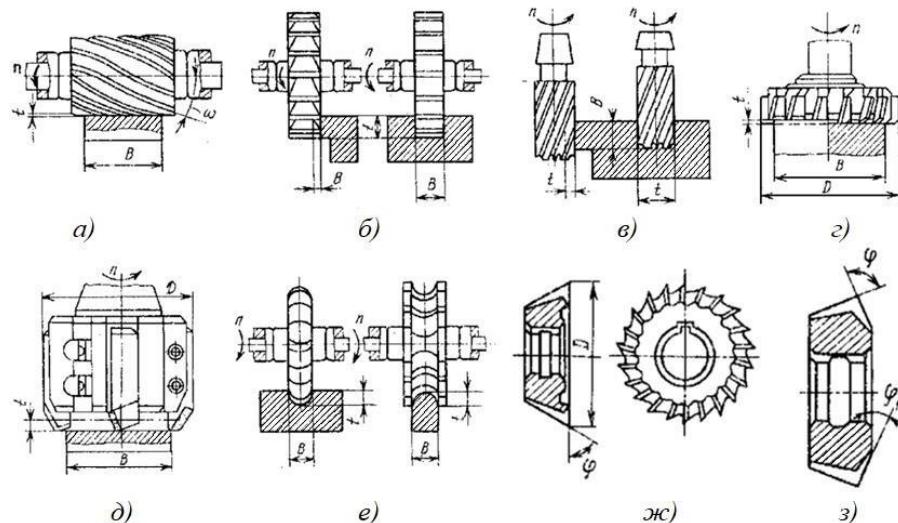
Типи фрез та схеми фрезерування на фрезерувальних верстатах з горизонтальною та вертикальною віссю шпінделя [29; 31]
